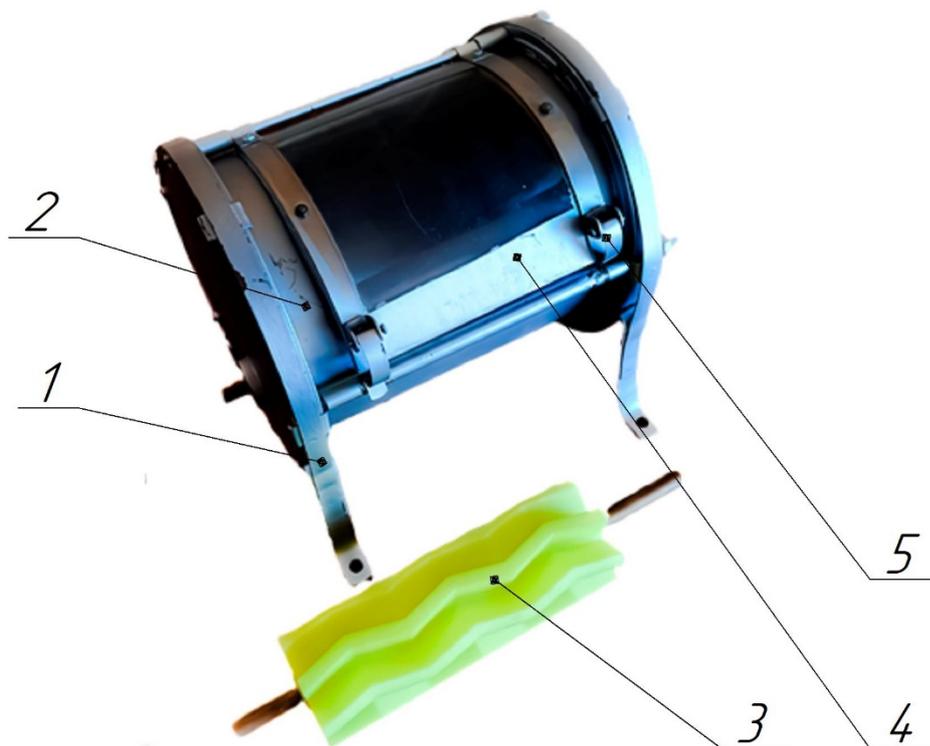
Общий вид маслоизготовителя: 1 – рама; 2 – ёмкость; 3 – роторно-лопастной рабочий орган; 4 – люк; 5 – фиксаторы
